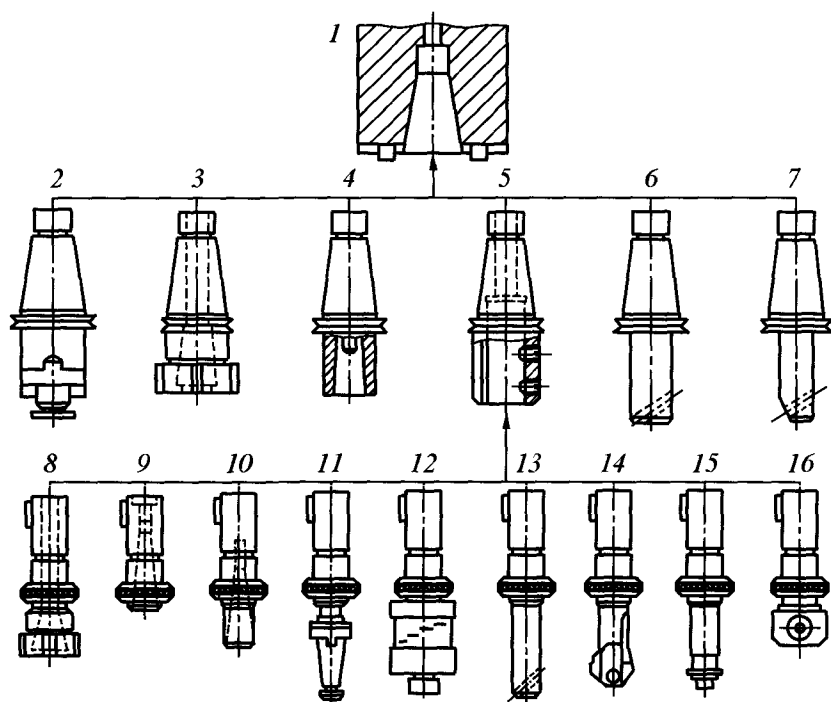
Система инструмента со сменными наладками для базирования и закрепления в базисном агрегате по цилиндрическому соединению с односторонним натягом: 1 – шпиндель станка; цельный вспомогательный инструмент; 2 – оправка для торцовых фрез; 3 – цанговый патрон; 4 – втулка с конусом Морзе; 6 и 7 – расточные оправки; базисный агрегат 5 и сменные наладки к нему: 8 – цанговый патрон; 9 и 10 – короткая и длинная втулки с конусом Морзе; 11 – оправка для насадных разверток; 12 – патрон для метчиков; 13 – расточная оправка; 14 – оправка первого сверла; 15 – оправка для расточных блоков; 16 – расточный патрон
